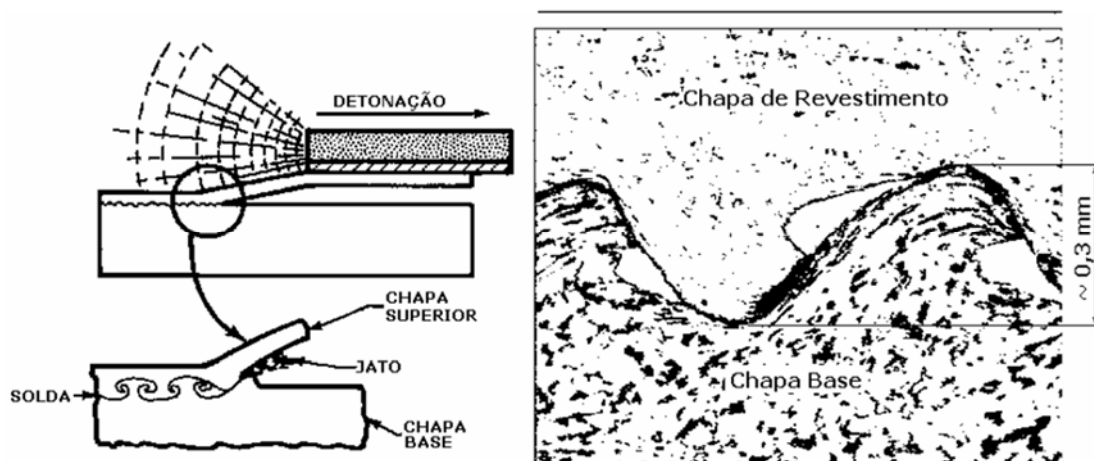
Processo de soldagem por explosão em ângulo e ondas na interface entre os dois componentes soldados[36].
